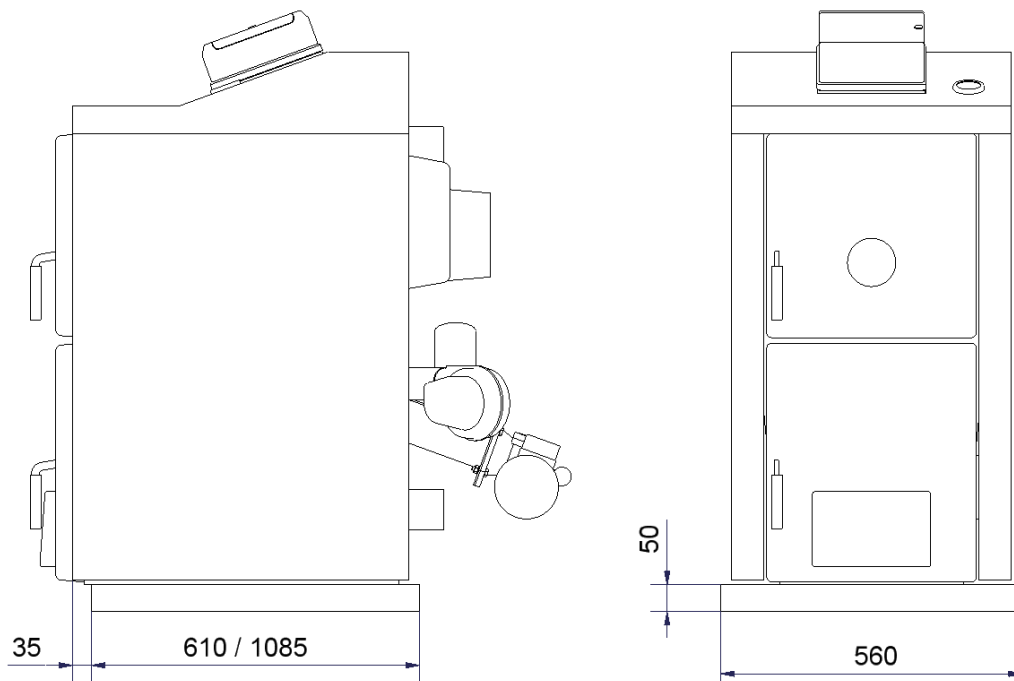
Dimensions du socle se trouvant sous le corps de la chaudière (CEDRA ECO 24/48)
